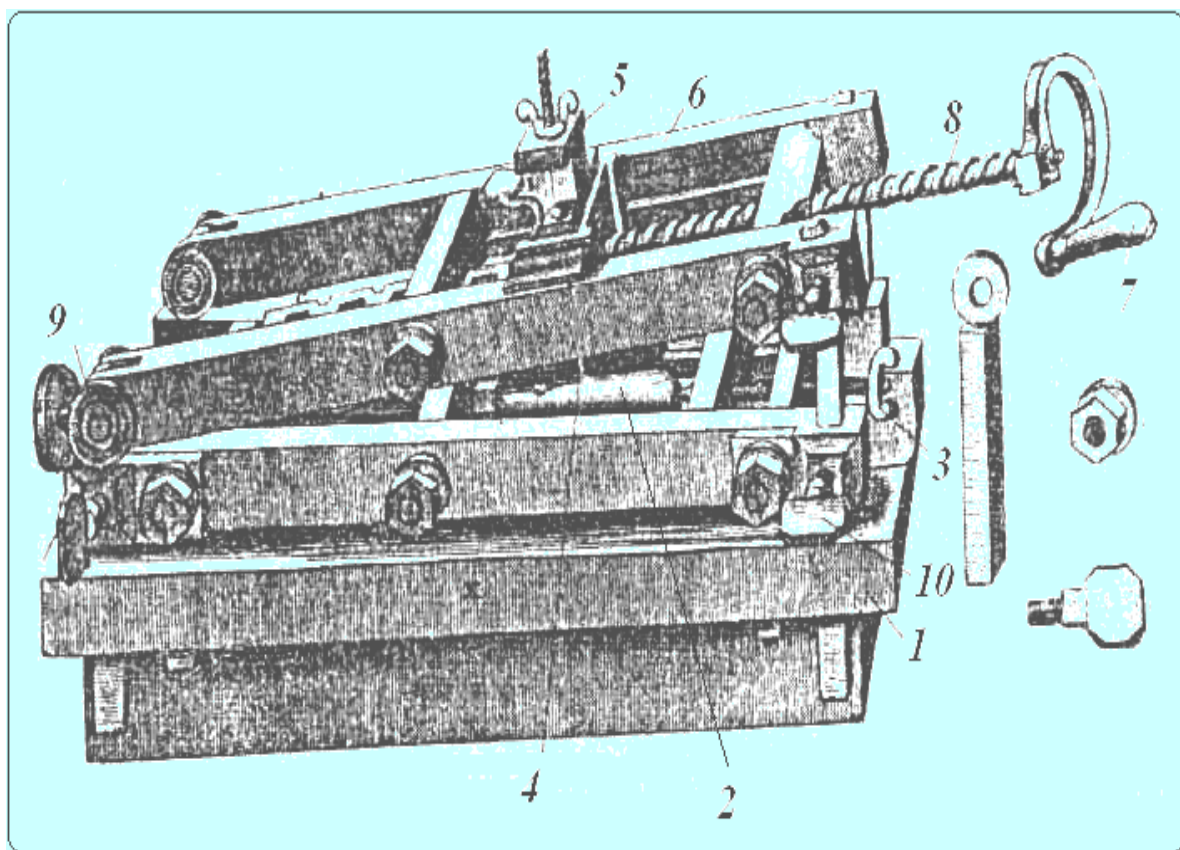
Универсально-строгальный станок (конструктор Ш. Плюмье, 1701 г.)
